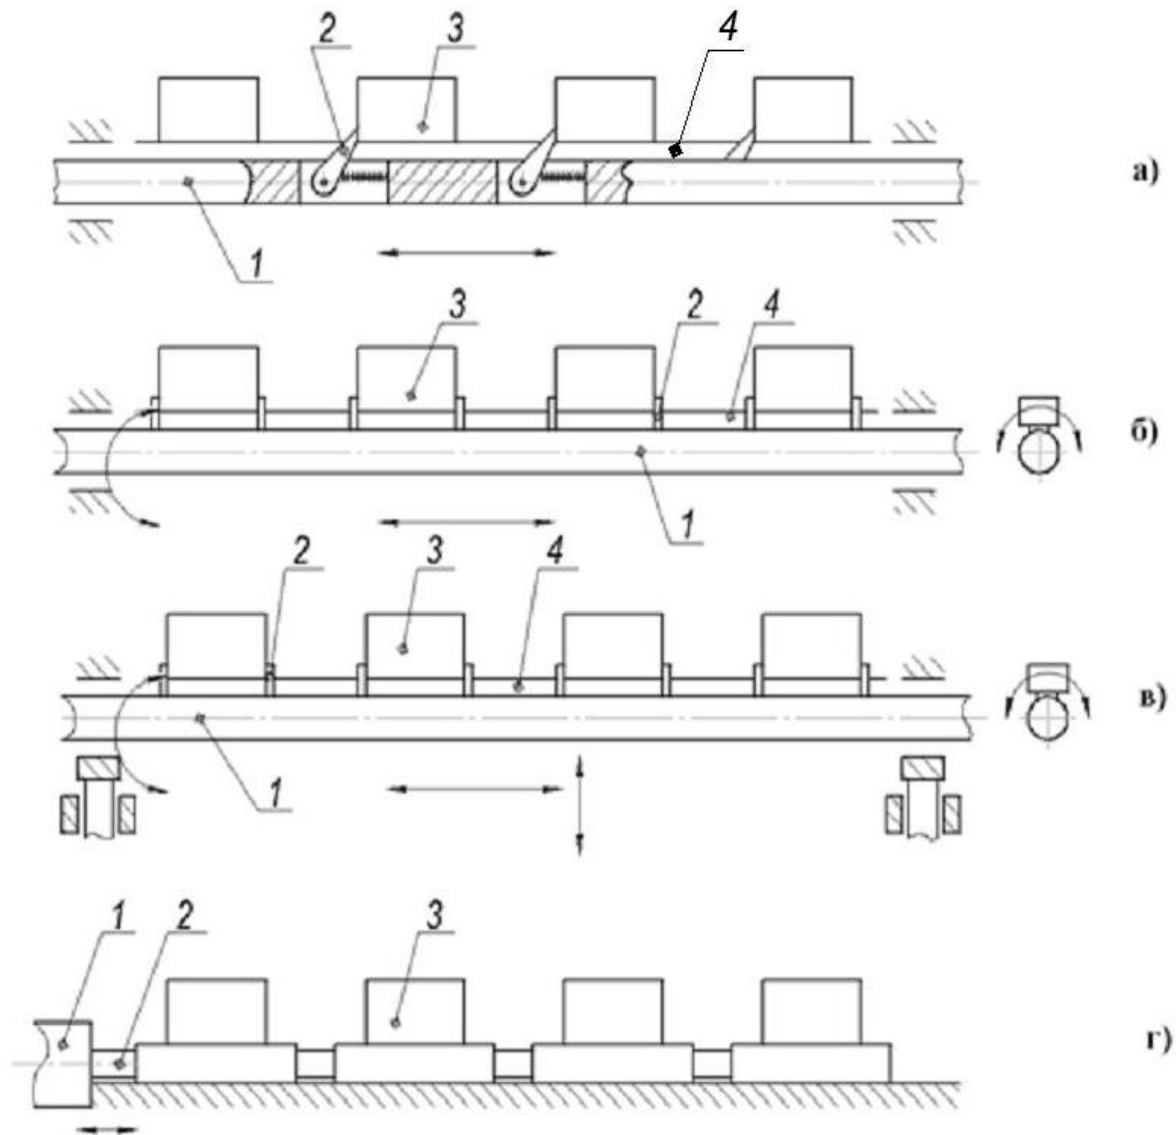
Види конструкцій крокових транспортерів: а – транспортер з собачками; б – транспортер з прапорцями; в – грейферний транспортер з прапорцями; г – штовхаючий транспортер
